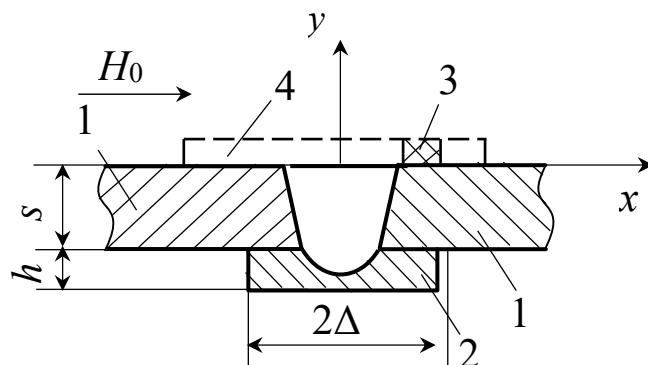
Сварной образец без выпуклости шва: 1 – свариваемые пластины; 2 – остающаяся подкладка; 3 – ленточный локальный магнитоноситель (ЛЛМ); 4 – места расположения ЛЛМ
